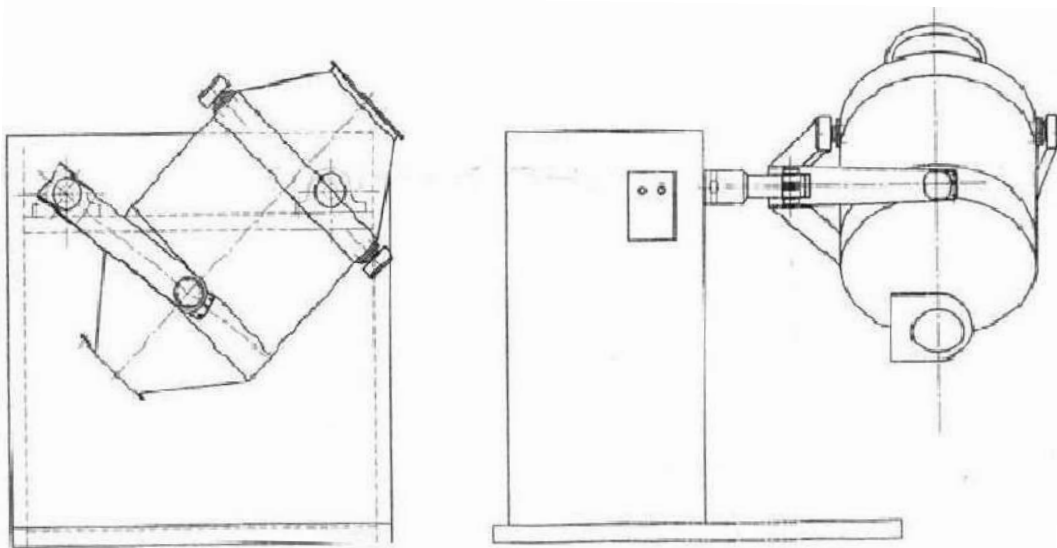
Схема смесителя для приготовления сухого ЗЦМ
